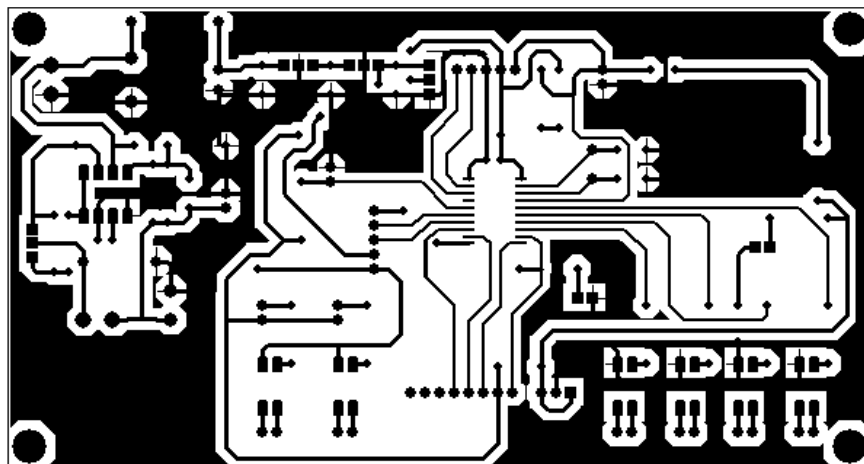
Diseño PCB del sistema electrónico de publicidad
